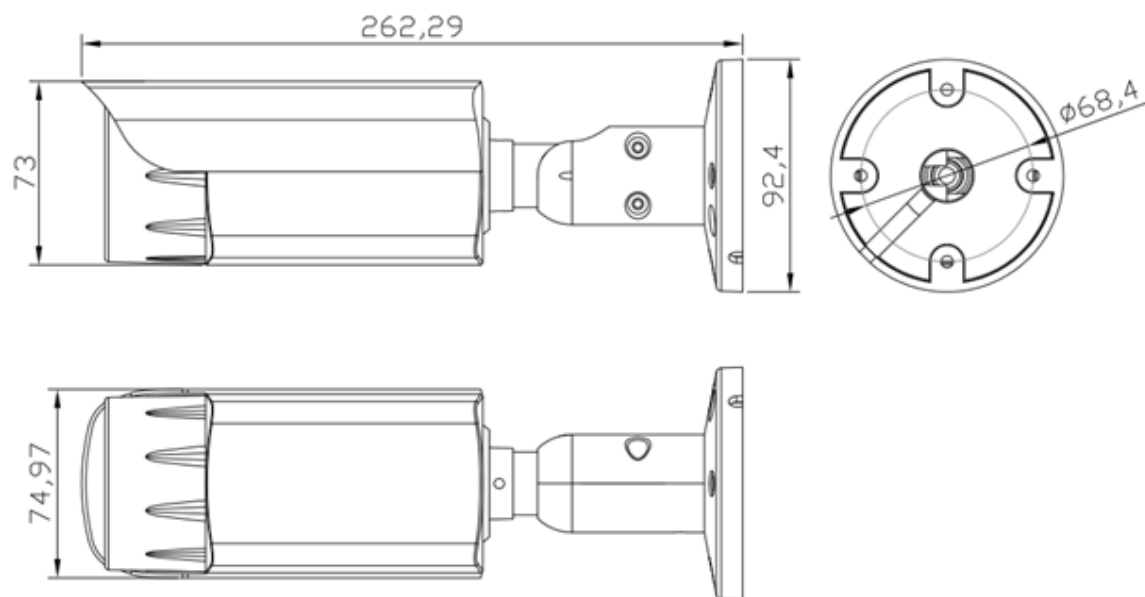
Габаритный чертеж видеокамеры ИВМС-501.
